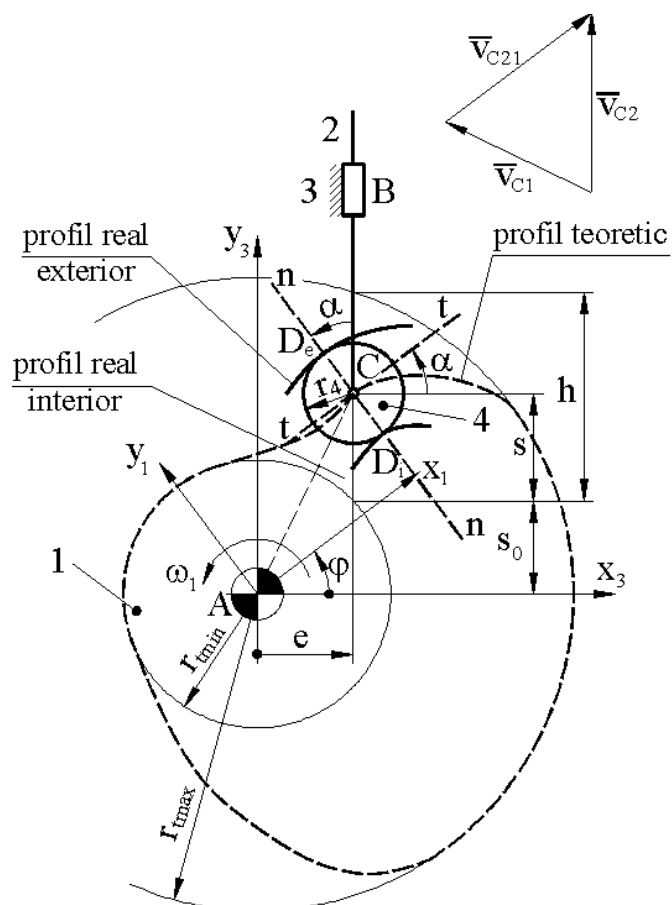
Mecanismul camă disc de rotație - tachtet de translație cu rolă [3.4], [3.6].
